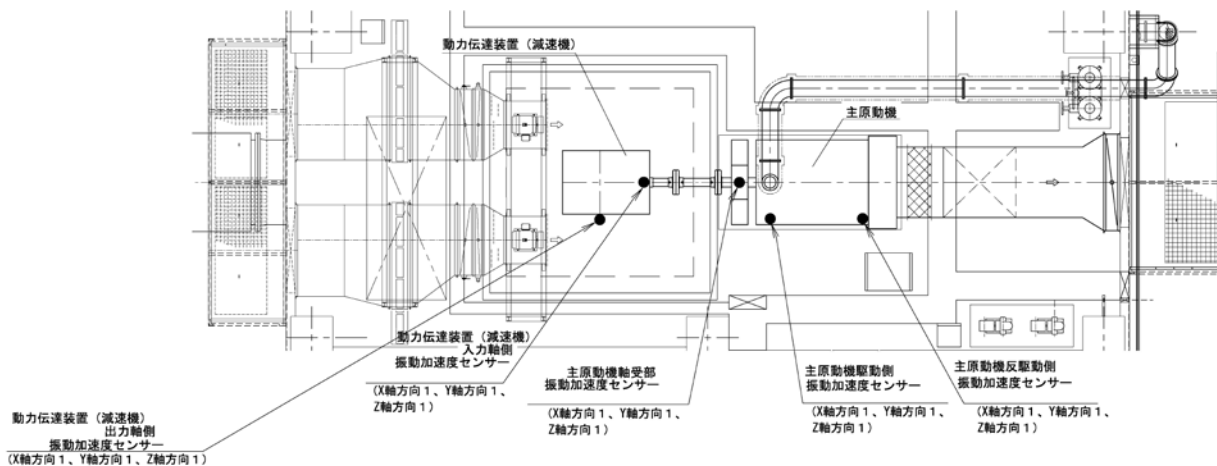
主原動機・減速機のセンサー取付位置図 (平面図)
